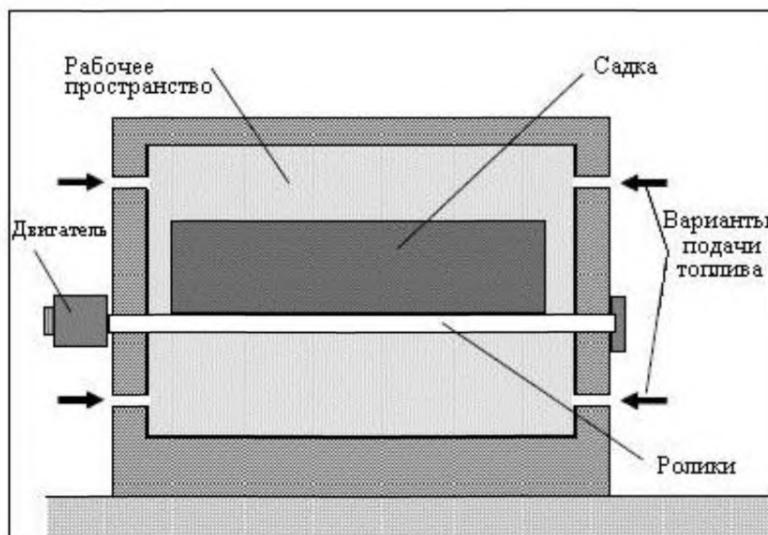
Вид роликовой печи в разрезе [80]
